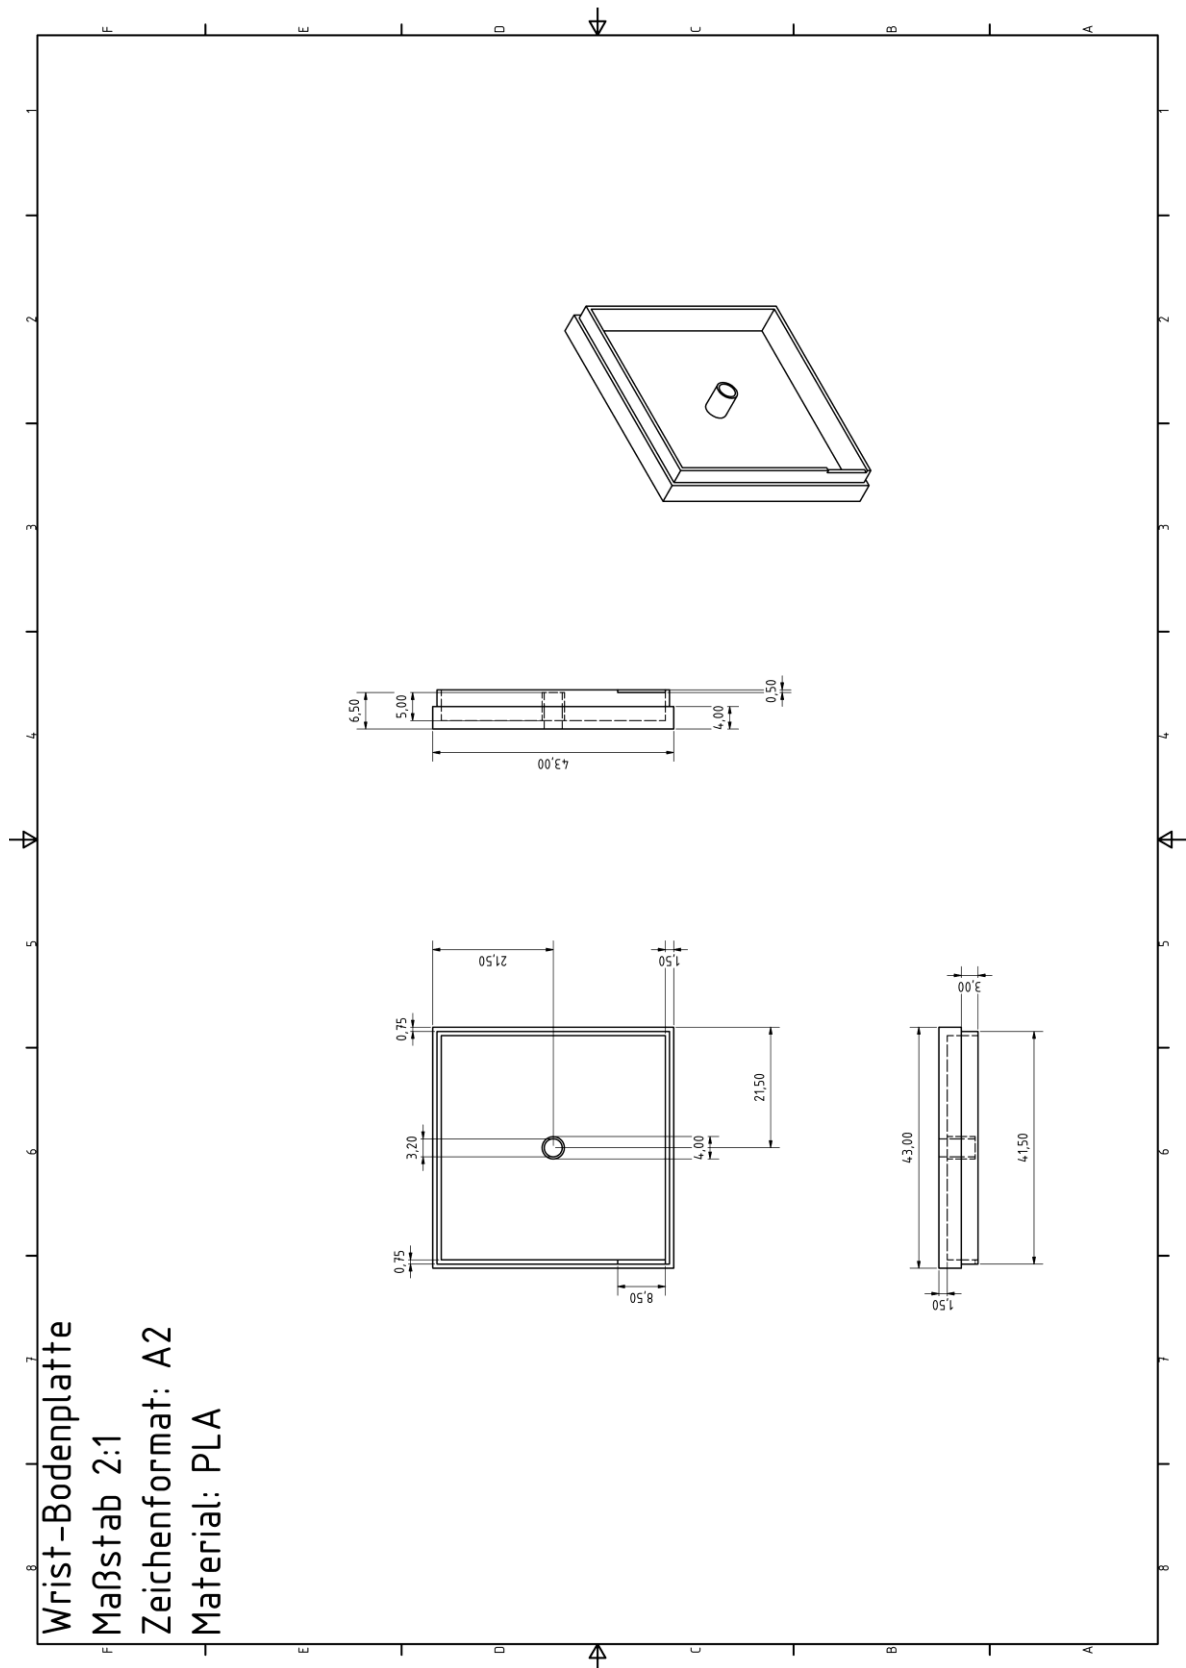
Konstruktionszeichnung Sensorsegment Bodenplatte
